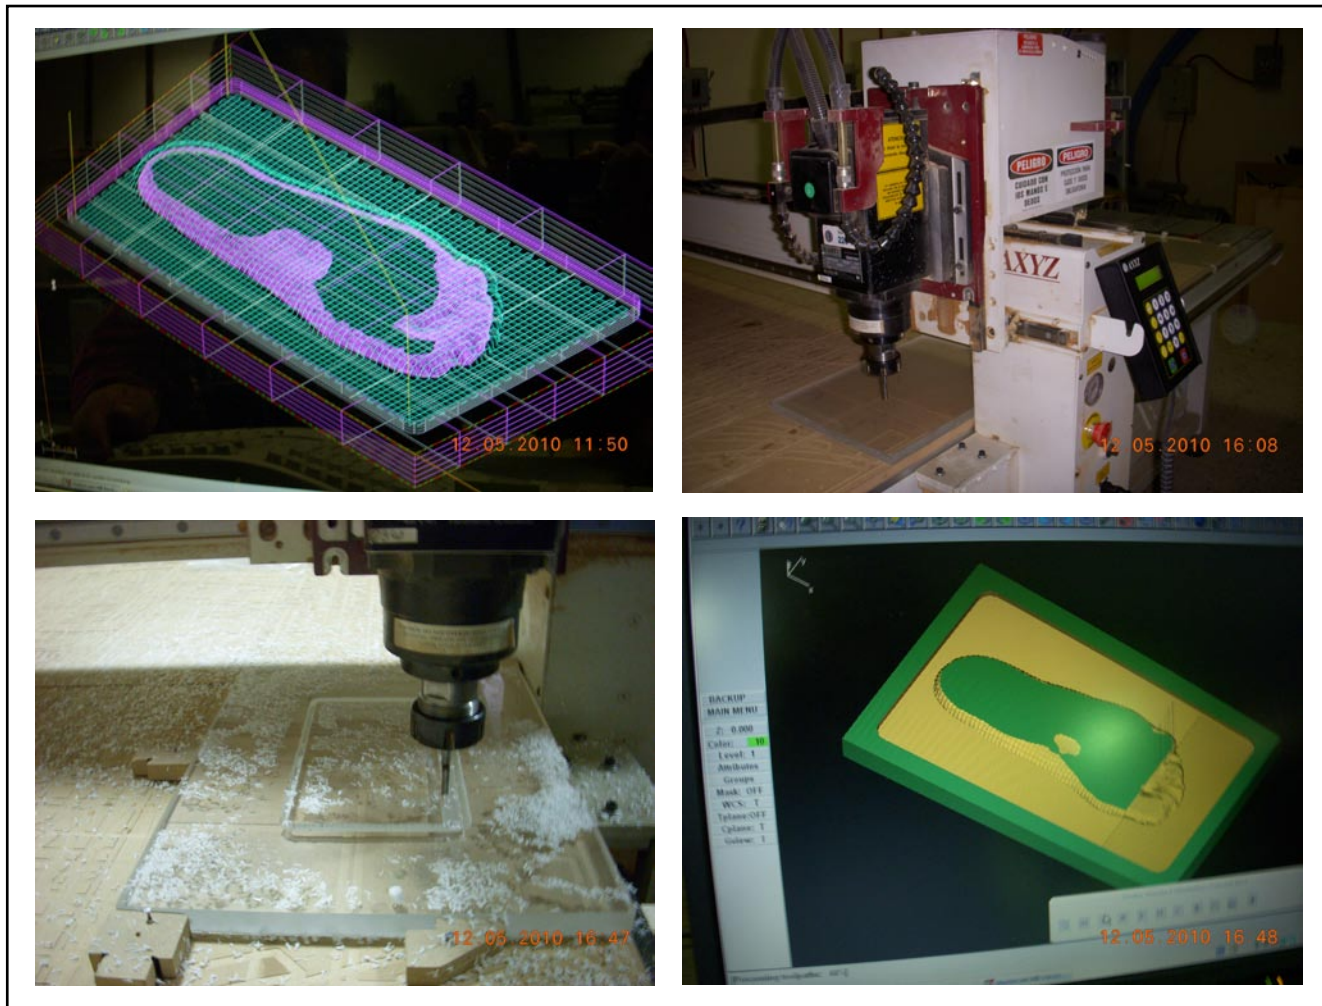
Proceso de manufactura de molde para prototipo de plantilla para pie plano
